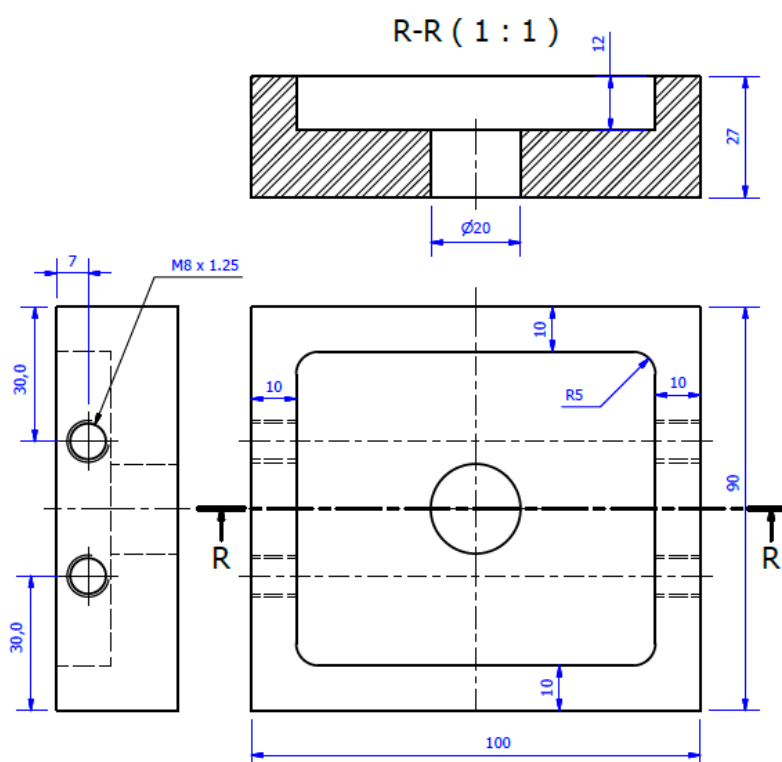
Especificações da peça de suporte para os blocos de soldagem
